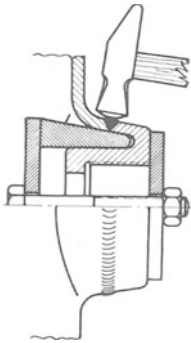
Vorrichtung zum Hämmern von Rundnähten.
